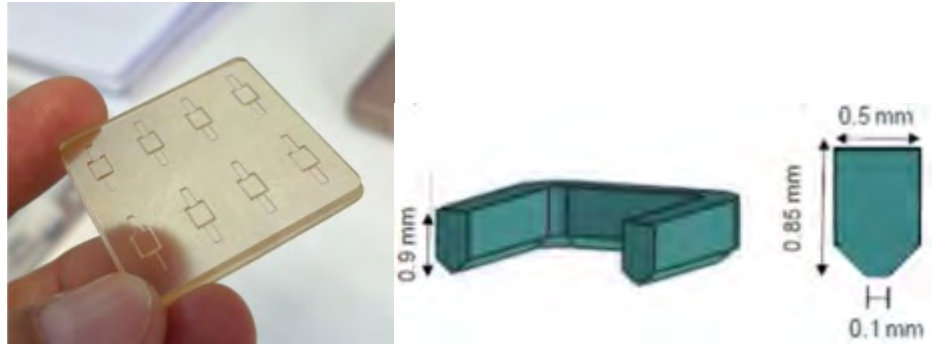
O-rings: molde de resina (izq.) y diseño deo-ring (der.).
